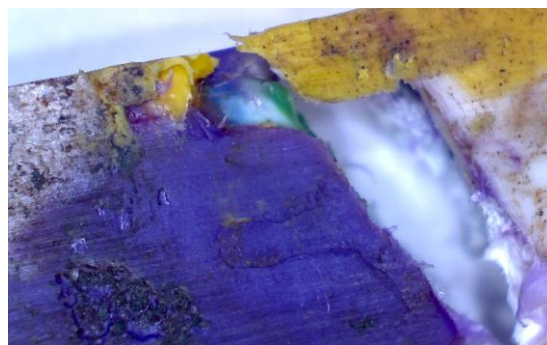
Imagen macroscópica de la zona de fractura de la placa HDPE Tetrapak multicolor M2
